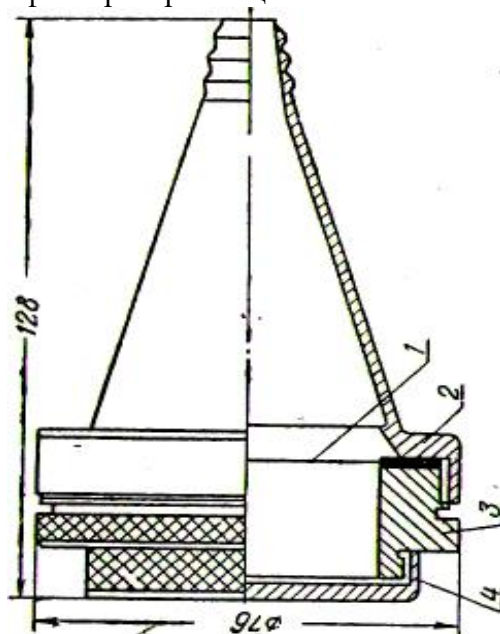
Металлический патрон для пылеулавливающего фильтра:
